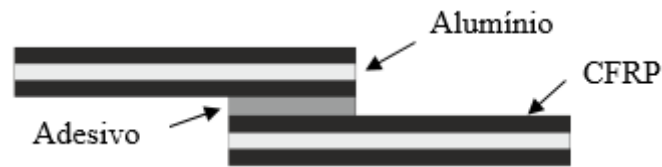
Configuração da junta CFRP-AL-CFRP, com um comprimento de sobreposição de 50 mm.
